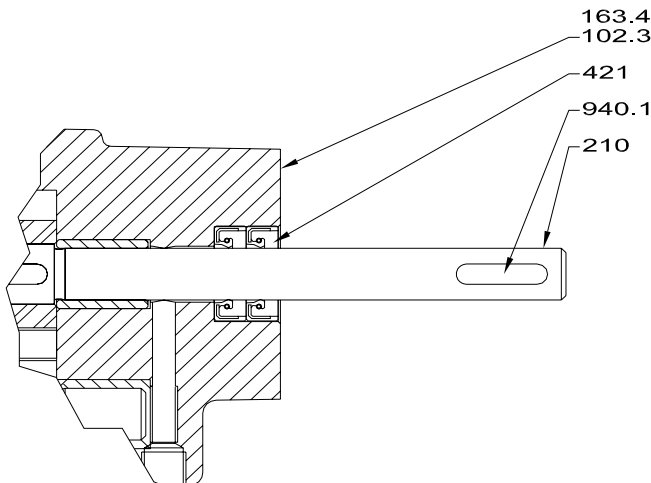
Desenho em Corte bomba FBE c/ retentor
